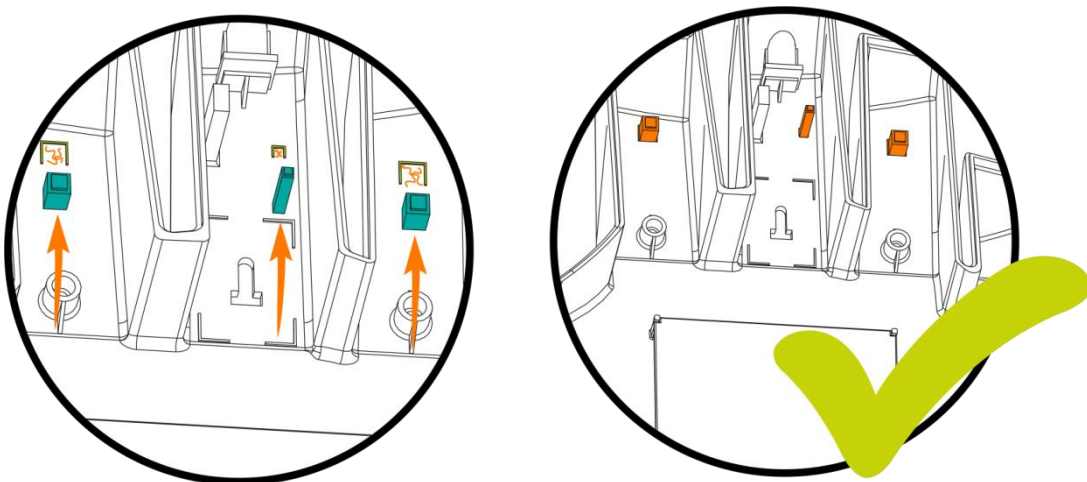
Ensamblaje 1.12, 1.13 – 1.4
